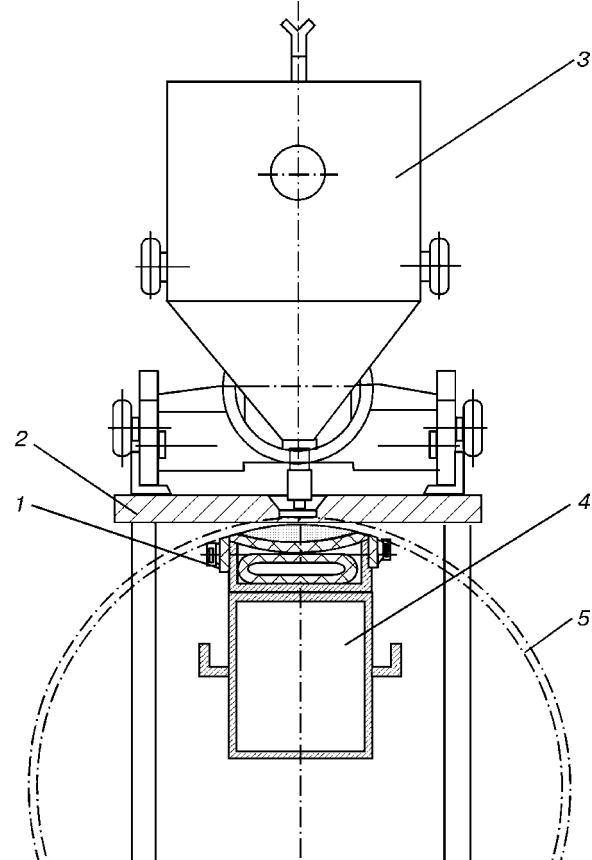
Схема установки для автоматической сварки под слоем флюса цилиндрических обечаек на флюсовой подушке: 1 — воздушный шланг; 2 — плита с направляющими; 3 — сварочный трактор; 4 — поворотная консоль с флюсовой подушкой; 5 — обечайка
